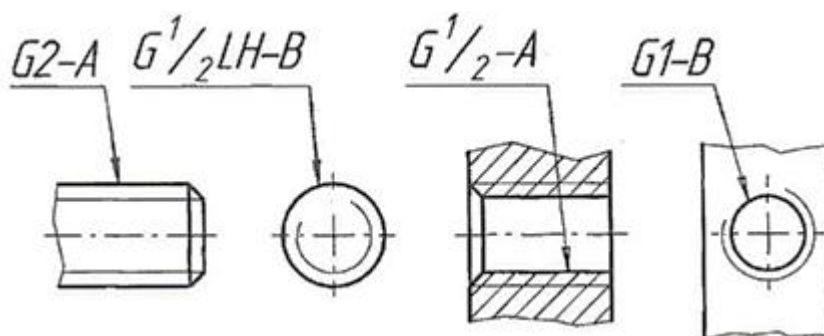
Обозначение трубной цилиндрической резьбы на чертежах
